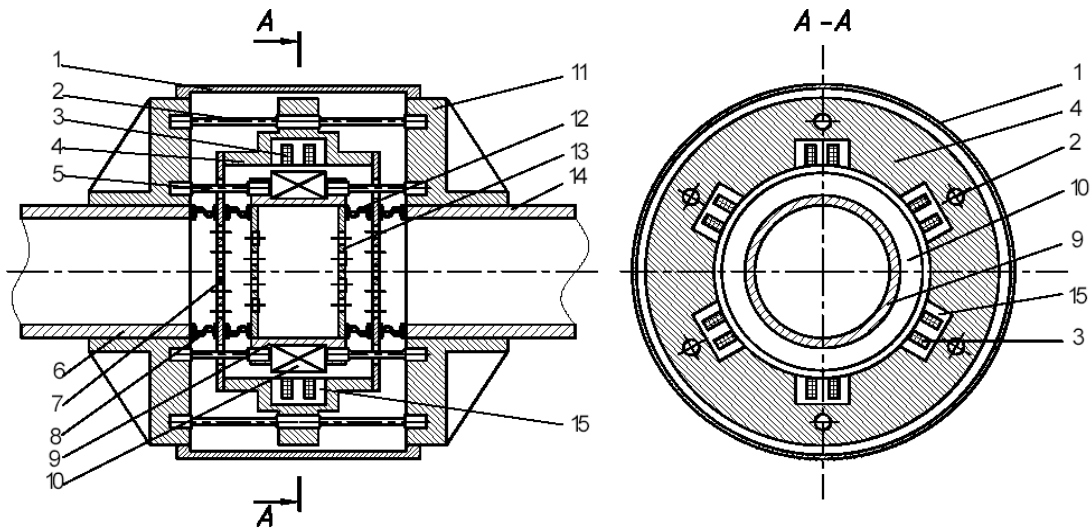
Принципова схема вібраційного електромагнітного кавітатора резонансної дії для магнітно-кавітаційного оброблення рідин: 1 – корпус; 2,5 – пружні стержні; 3 – обмотка; 4 – корпус статора; 6 – труба; 7,13 – деки; 8,12 – пружні елементи; 9 – камера; 10 – ярів; 11 – реактивна маса; 14 – труба; 15 – котушки електромагнітів
